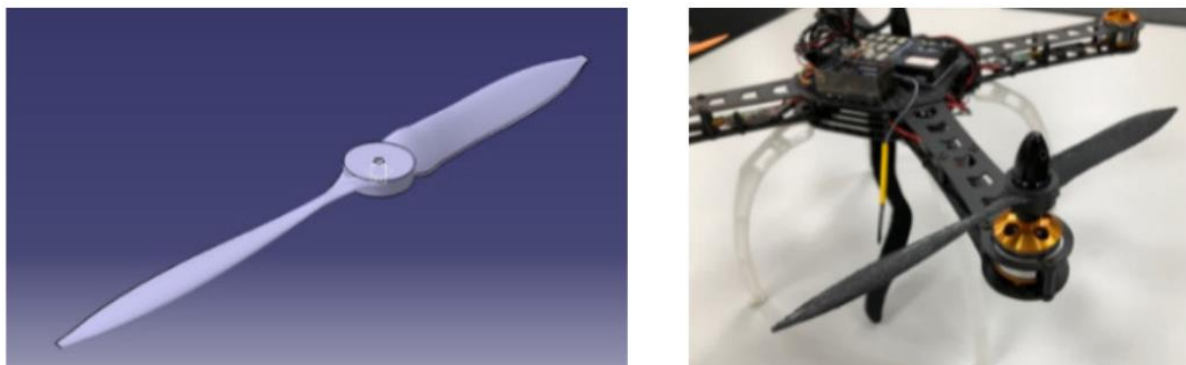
Винты БПЛА, изготовленные с помощью FDM 3D-печати [17]
